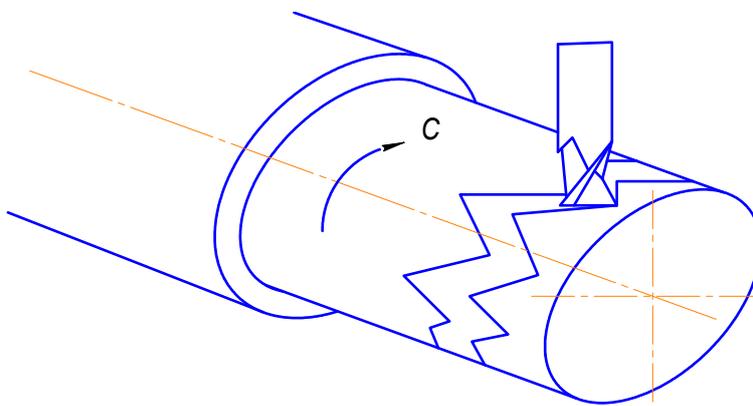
Цилиндрическая интерполяция при фрезеровании
